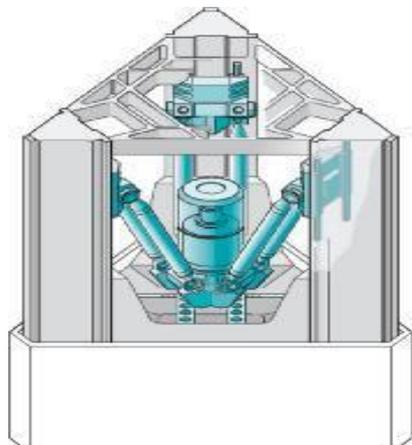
Токарный станок мод. V100 на базе МПС фирмы Index-Werke (ФРГ)
